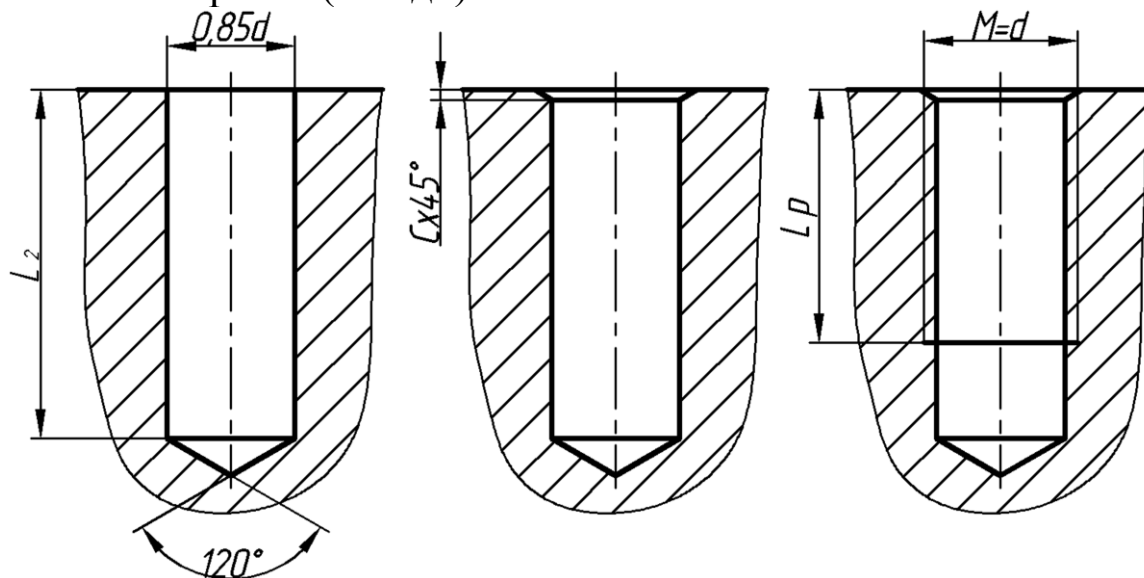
Отверстие с резьбой для шпилечного и винтового соединений
